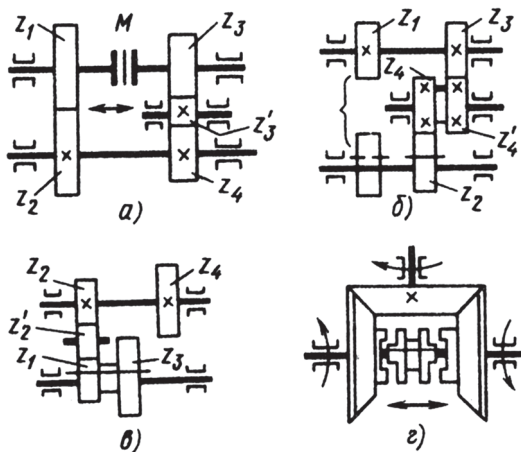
Кинематические схемы (а-г) реверсивных механизмов
